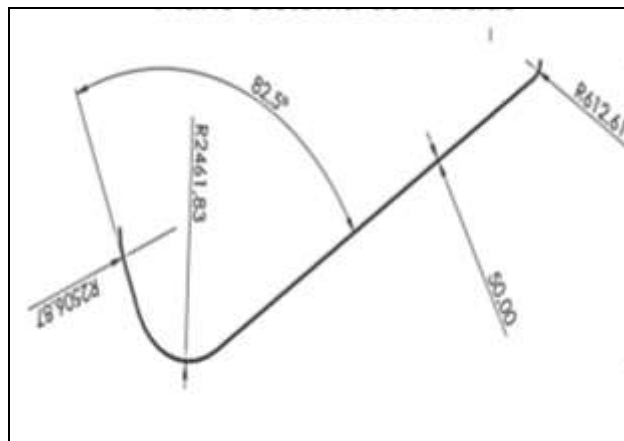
Plano superior del sistema de filtrado. *Autoría propia
